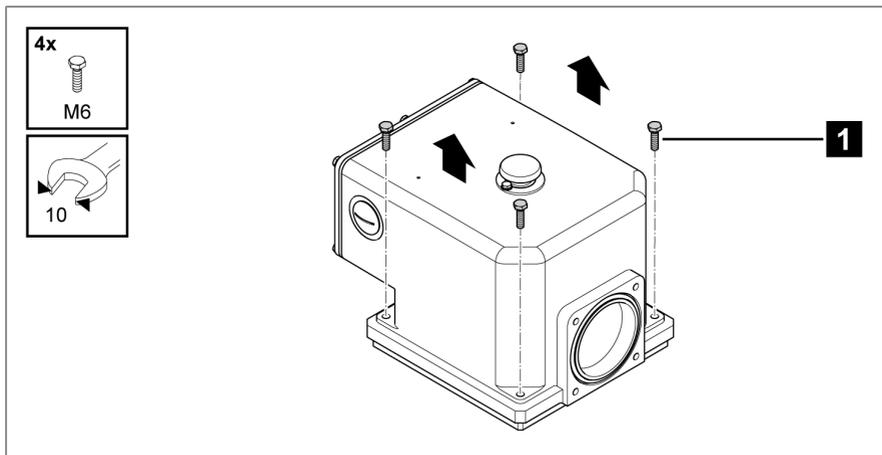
Befestigungsschrauben Abdeckhaube lösen
